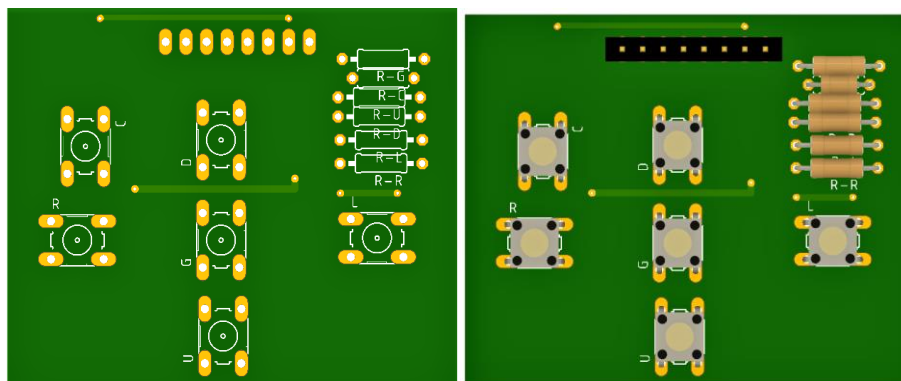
Prototipo del diseño PCB de las direccionales. Fuente Propia
